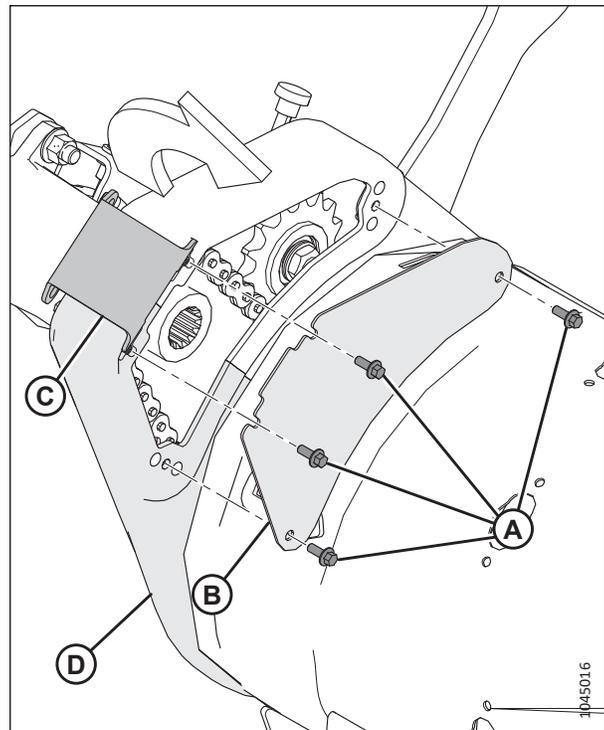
Einzugstrommelgetriebe – Rückansicht
